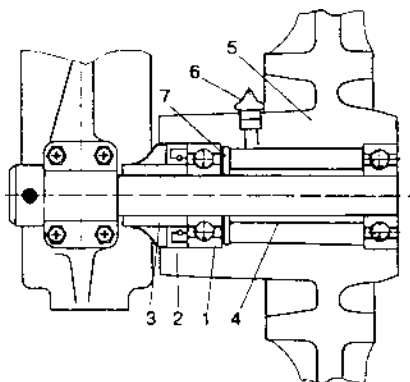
Установка пресс-масленки в ступицу переднего колеса “Иж-05-015”:
